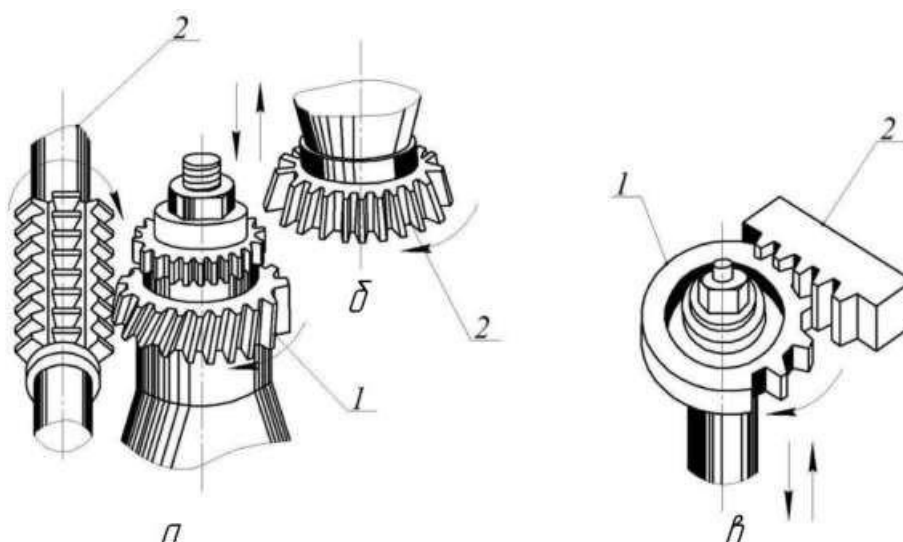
Схеми нарізування циліндричних зубчастих коліс методом обкатування: а – черв’ячною фрезою; б – дисковим довб’яком; в – гребінкою; 1 – зубчасте колесо; 2 – інструмент
